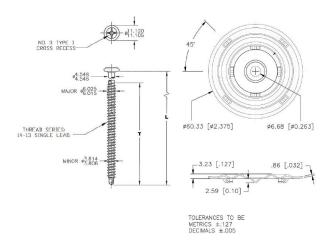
Vis Firestone "ALL PURPOSE" FASTENER + plaquette de fixation FIRESTONE HD SEAM PLATE
